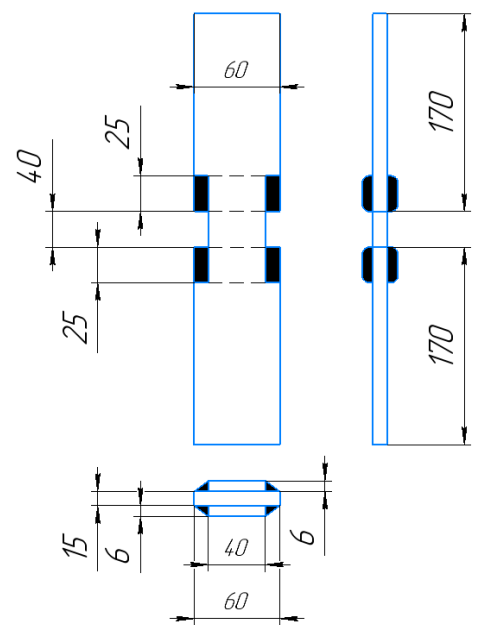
Загальний вигляд зразка з накладними повздовжніми кутовими швами
